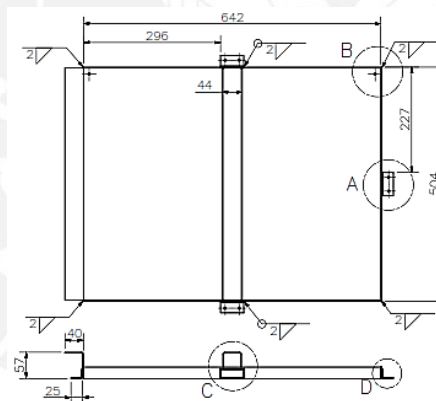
Plano de Bandeja de entrada – Plano PD1.1.3-A2
